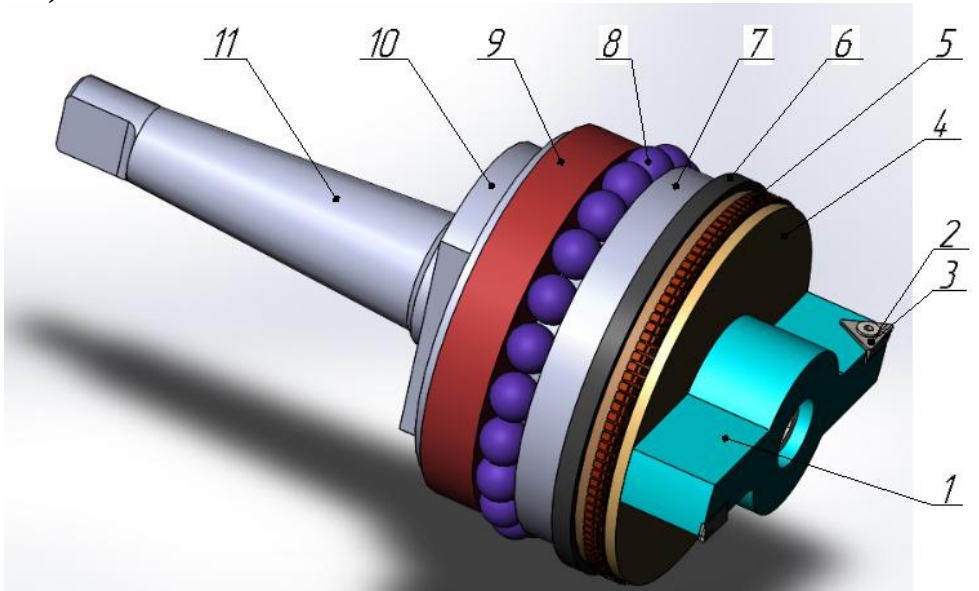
3D-модель магнитно-динамического инструмента для совмещенной обработки: 1 – расточная головка; 2 – режущая пластина; 3 – винт; 4 – уплотняющее кольцо; 5 – щетка; 6 – фетровая втулка; 7 – щечка; 8 – деформирующий элемент; 9 – магнитная система; 10 – гайка; 11 – конус Морзе
